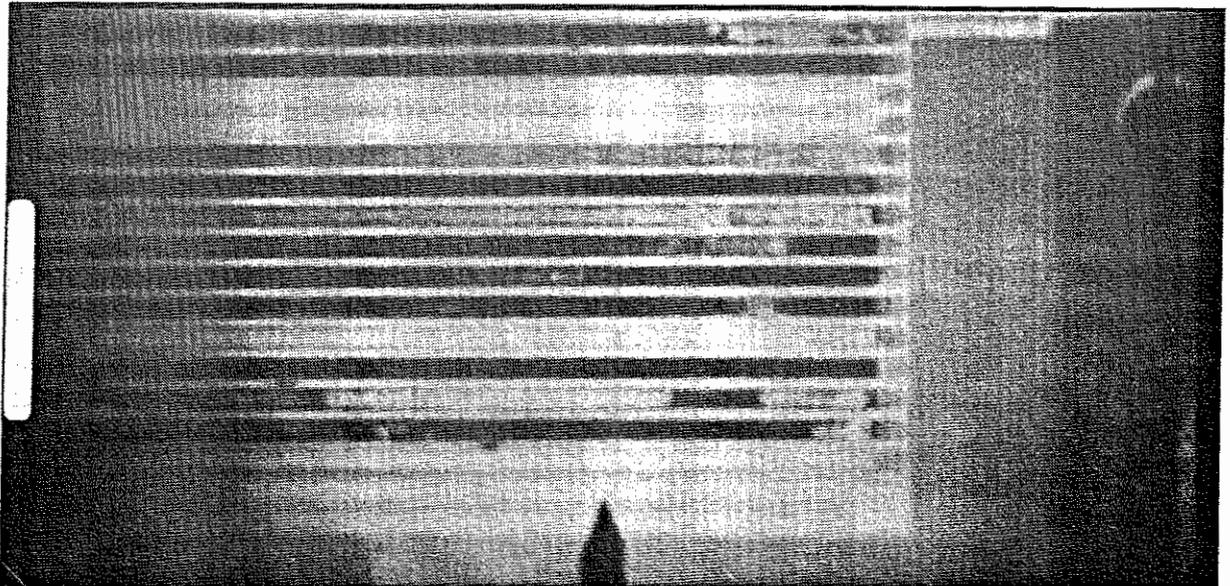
Neutronenradiographie, oberer Abschnitt eines Blattes des Siedewasserreaktor-Steuer-elementes
